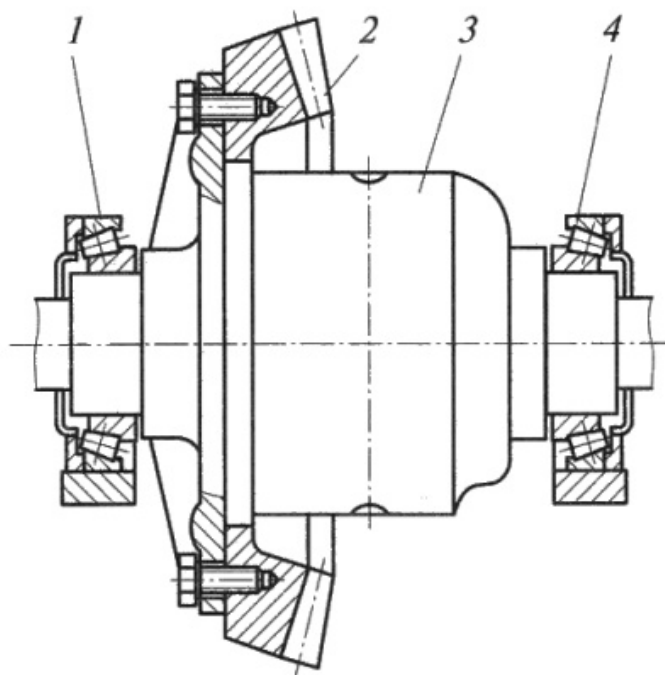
Установка ведомой шестерни конической главной передачи:
